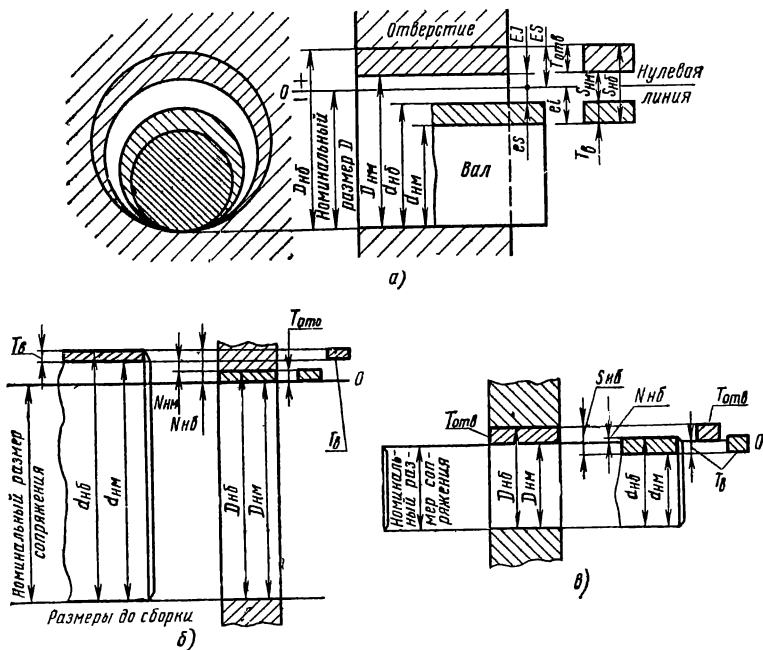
Схема изображения полей допусков: посадки: а — с зазором, б — с натягом, в — переходная
